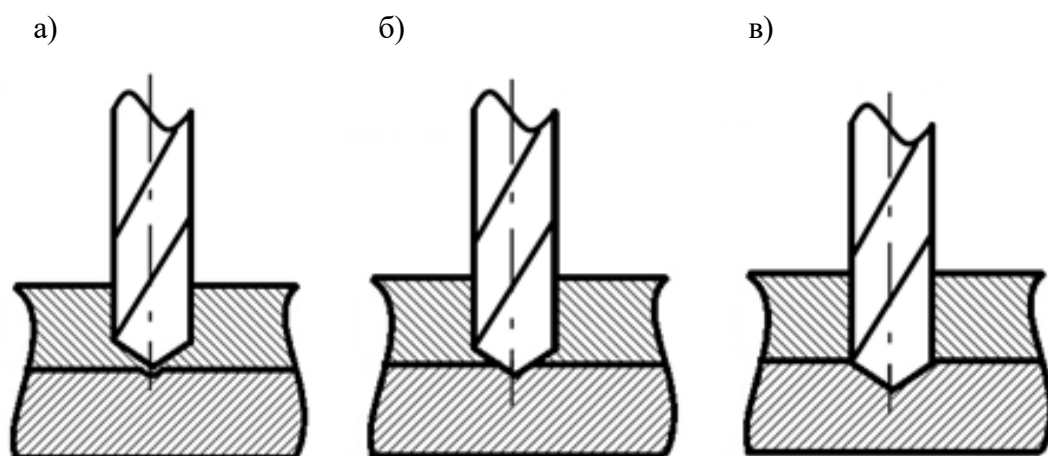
Серии экспериментов: а – сверление отверстий в верхнем слое пакета до утончения доньшка отверстия; б – сверление отверстий в верхнем слое пакета до прорыва доньшка отверстия; в – сверление отверстий до полного выхода заборного конуса сверла из верхнего слоя пакета
